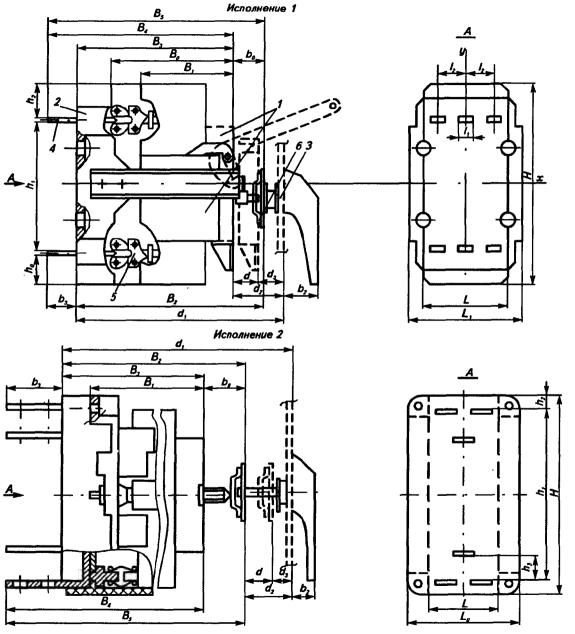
Габаритный чертеж выключателей выдвижного исполнения с механической блокировкой с ручным или электромагнитным приводом (вариант I)
